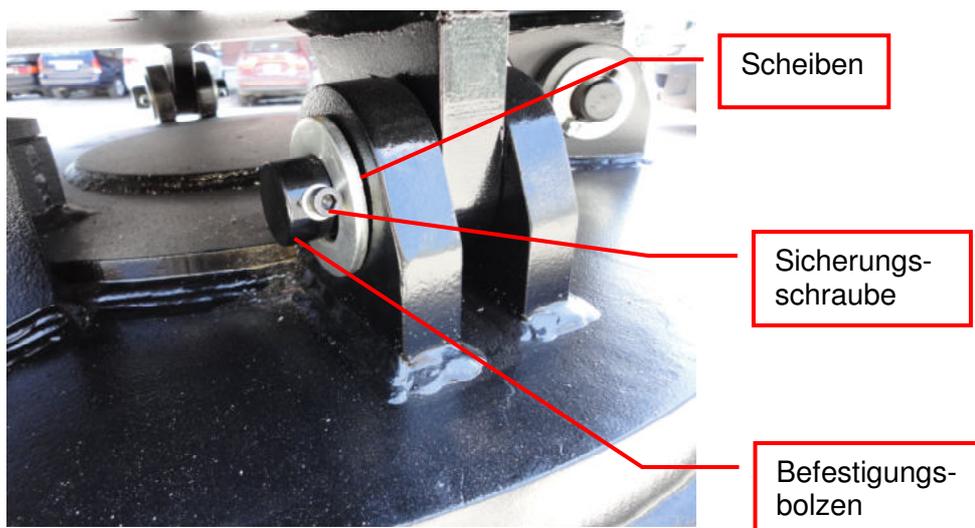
Befestigungsbolzen der Magnetplatte
